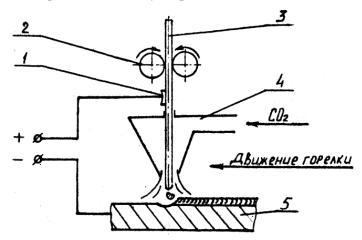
Схема сварки (наплавки) в углекислом газе: I – контакт подвода сварочного тока к присадочной проволоке; 2 – механизм подачи проволоки; 3 – электродная проволока; 4 – сопло сварочной горелки с подводом защитного газа; 5 – деталь
